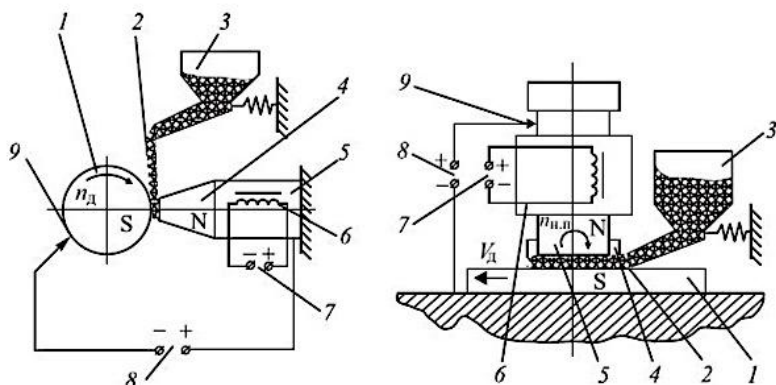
Принципиальная схема электромагнитной наплавки на поверхность заготовки детали типа тела вращения (а) и плоские поверхности (б):
